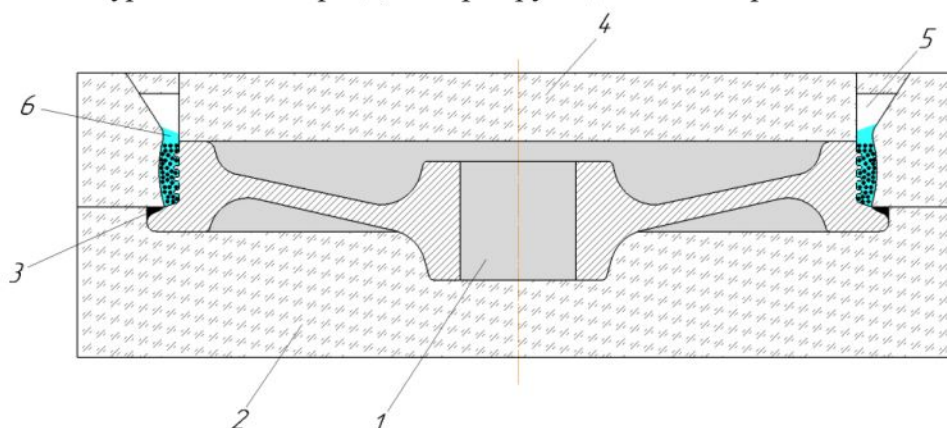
Схема заливки жидкого ПУ на поверхность катания колеса:
